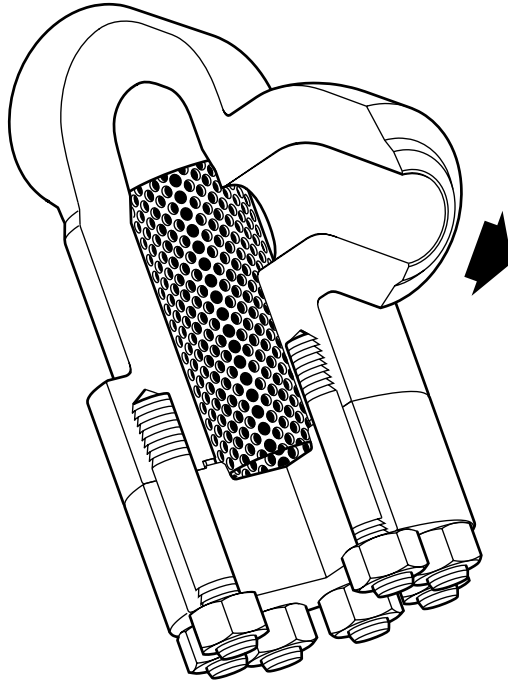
Filtro tipo 'Y' Fig 18HP, acero aleado, conexiones para soldar butt weld.
